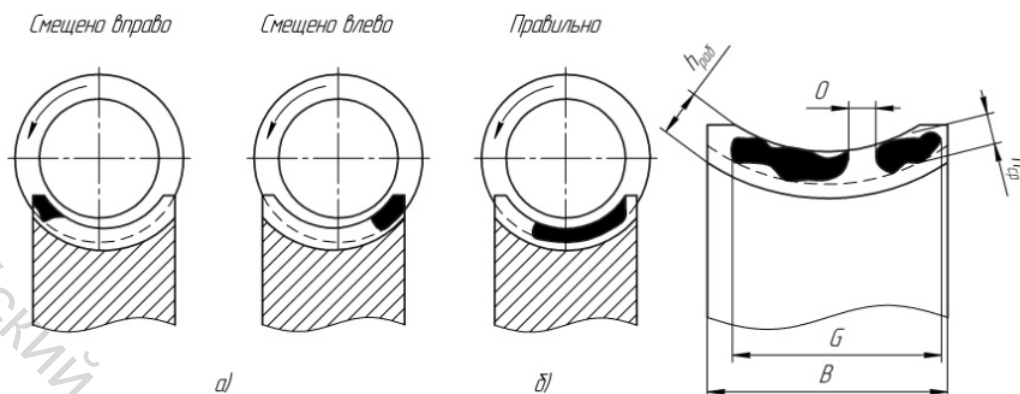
Виды отпечатков на зубьях червячного колеса при проверке зацепления на краску
